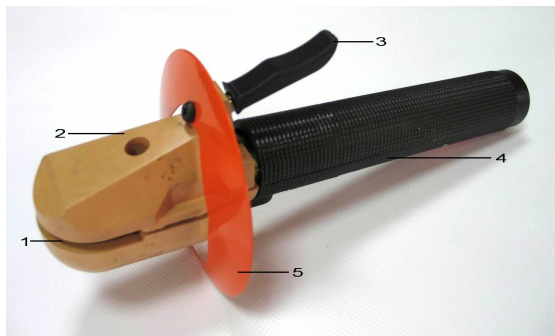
Электрододержатель ЭД-60 «Корд-Универсал»: 1 – ложемент; 2 – защитная крышка; 3 – рычаг; 4 – рукоятка; 5 – защитный экран
